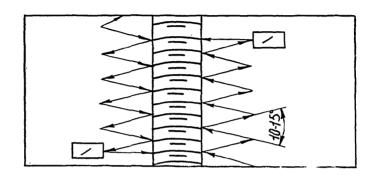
Схема перемещения искателя по поверхности при контроле сварного шва
